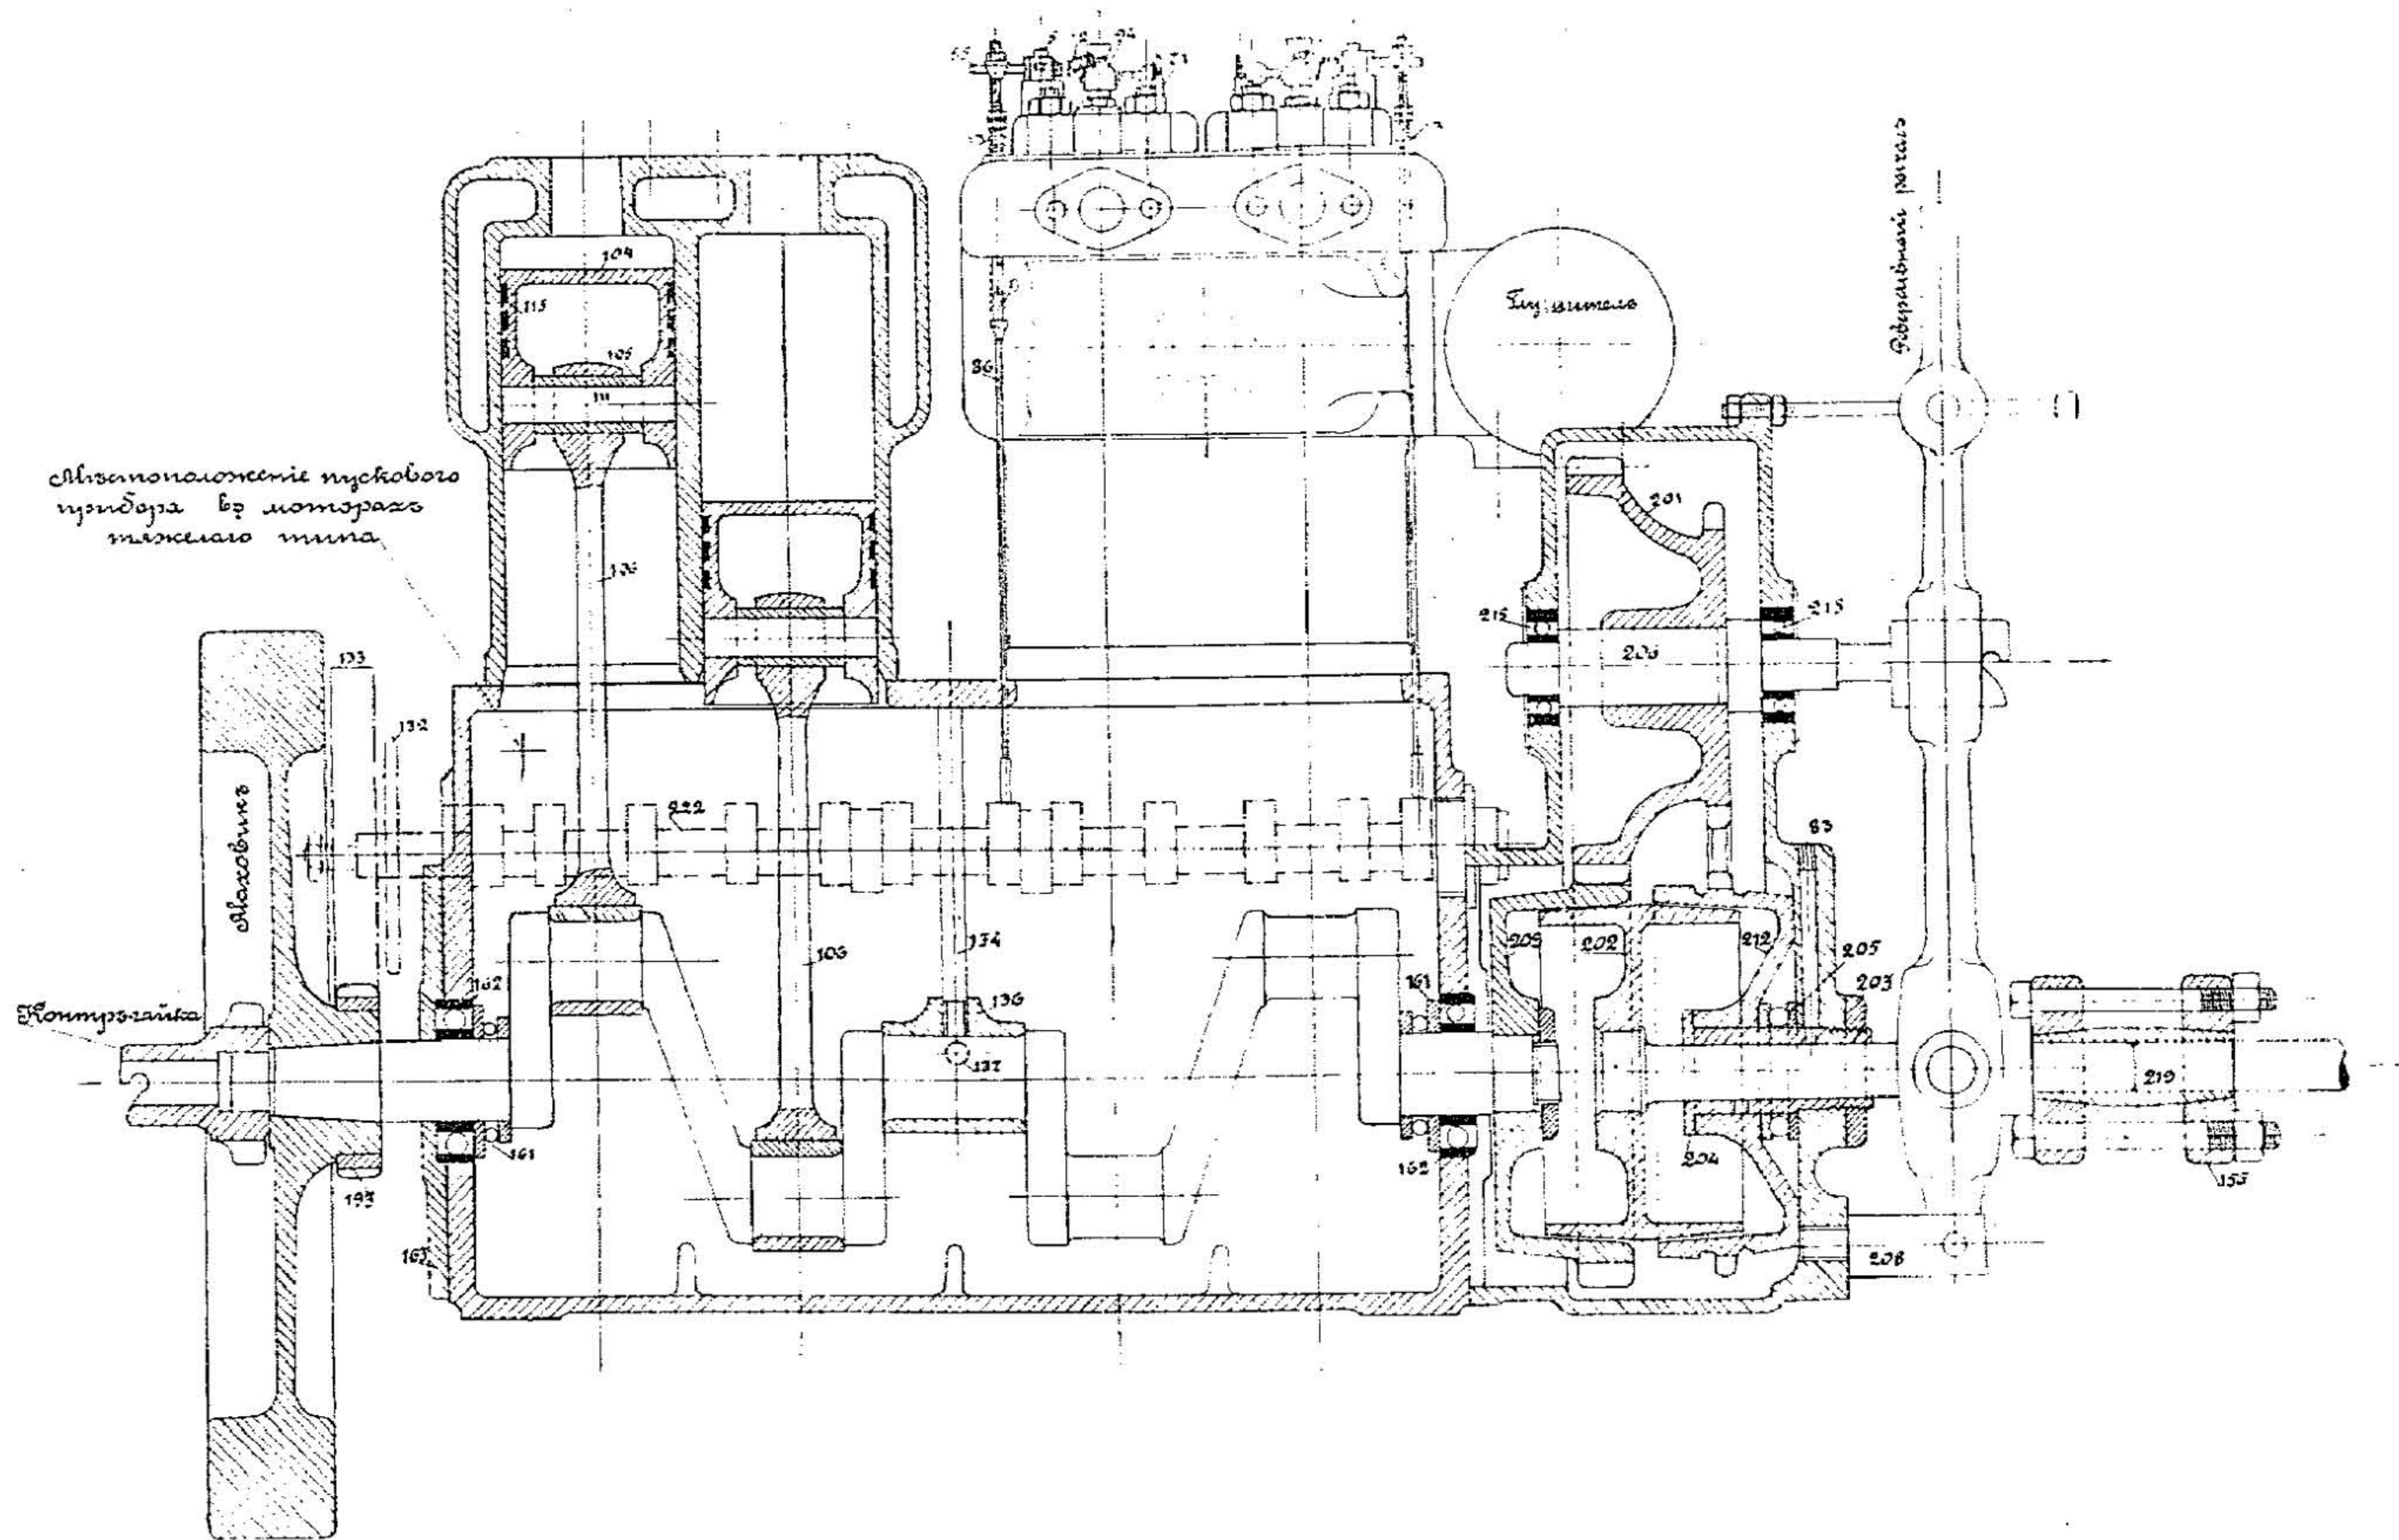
Разрѣзъ двигателя Кельвинъ.
